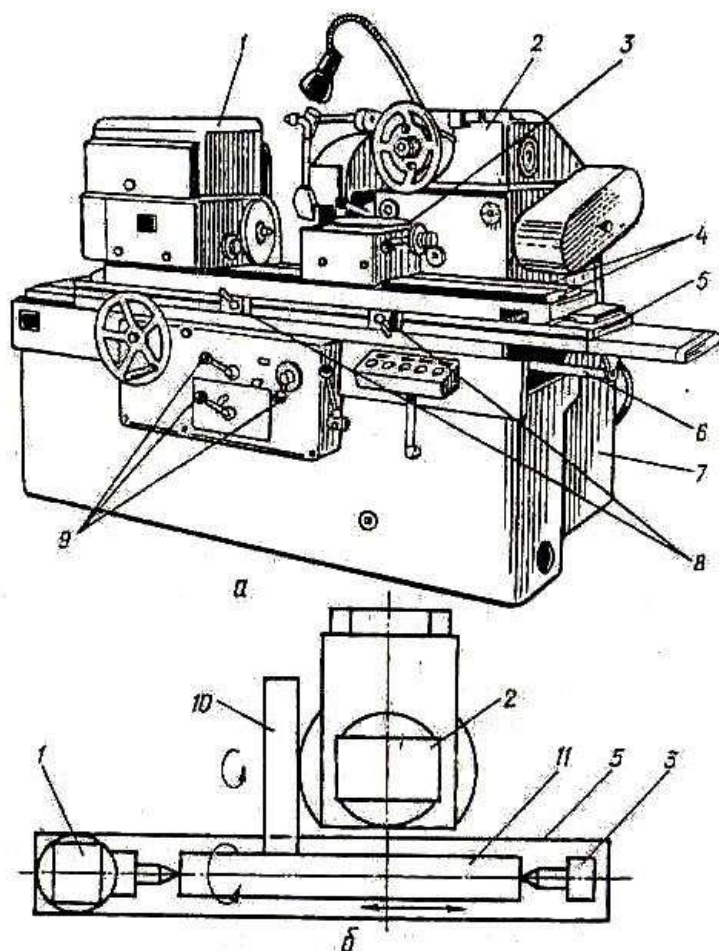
Круглошліфувальний верстат 3151: а – загальний вигляд; б – схема роботи
